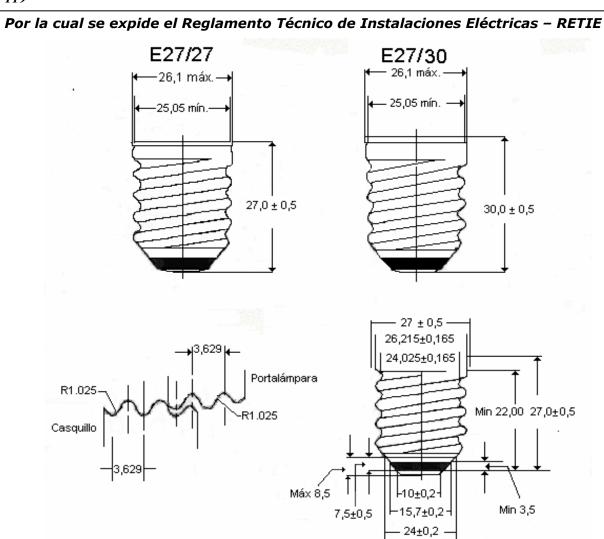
Dimensiones del casquillo de una bombilla en mm.
